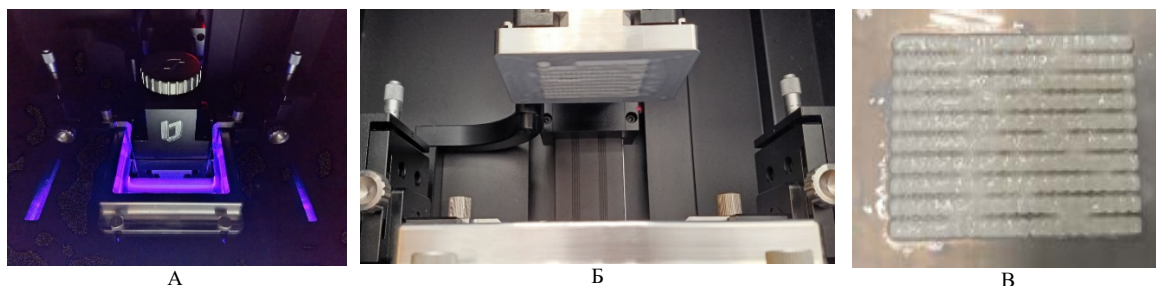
Процесс керамической печати (А) и размещение образцов на поверхности стола 3D-принтера (Б, В)
